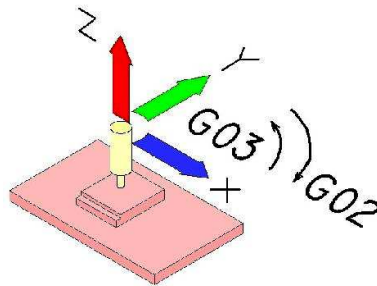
Ejes que se utilizan en un centro de maquinado.
